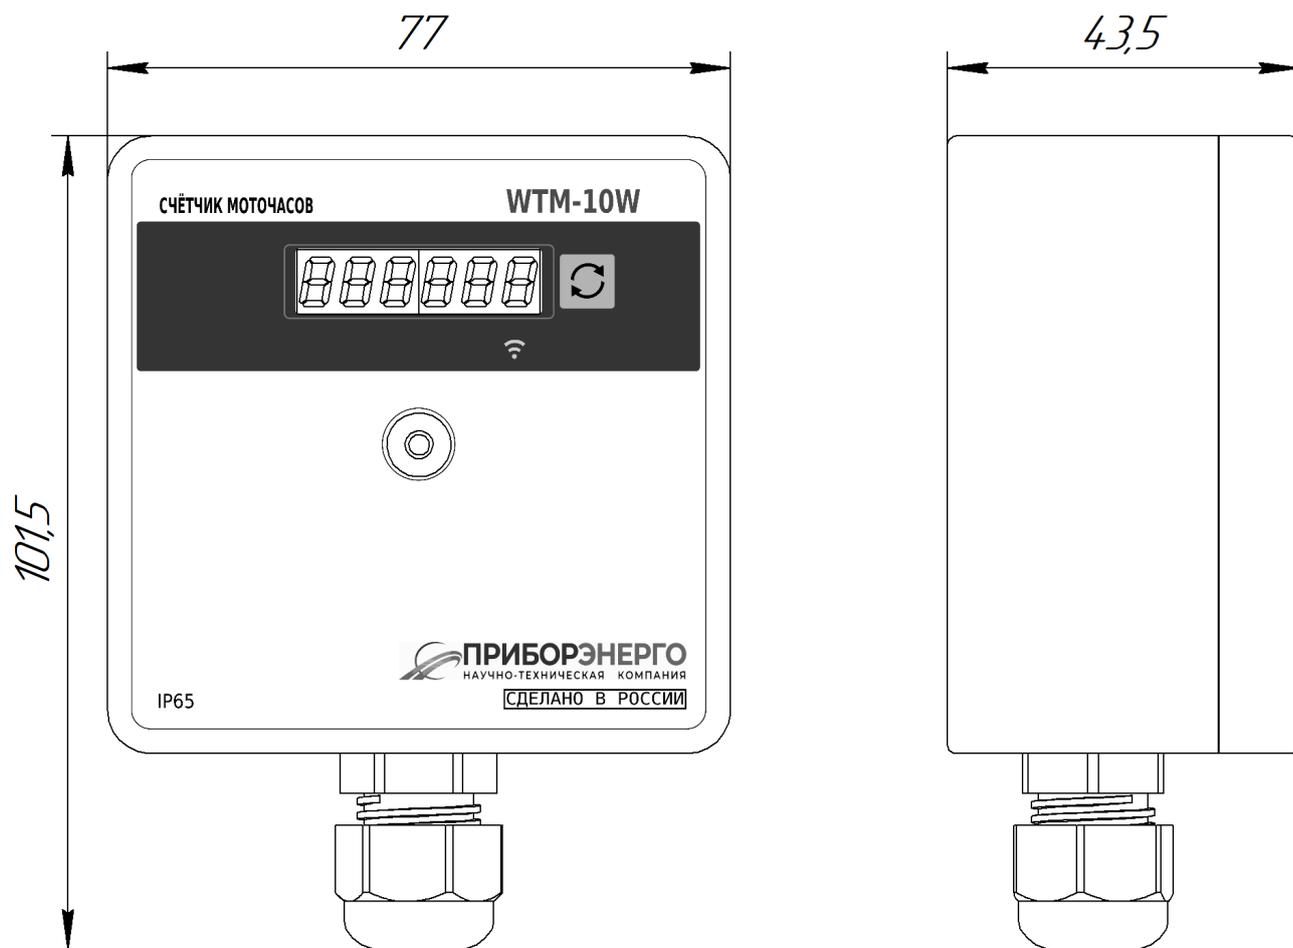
Габаритные размеры счётчика моточасов WTM-10W
